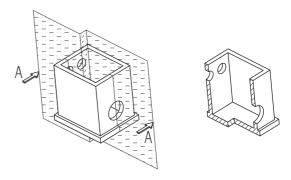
principe de la coupe brisée, coupe à plans parallèles
